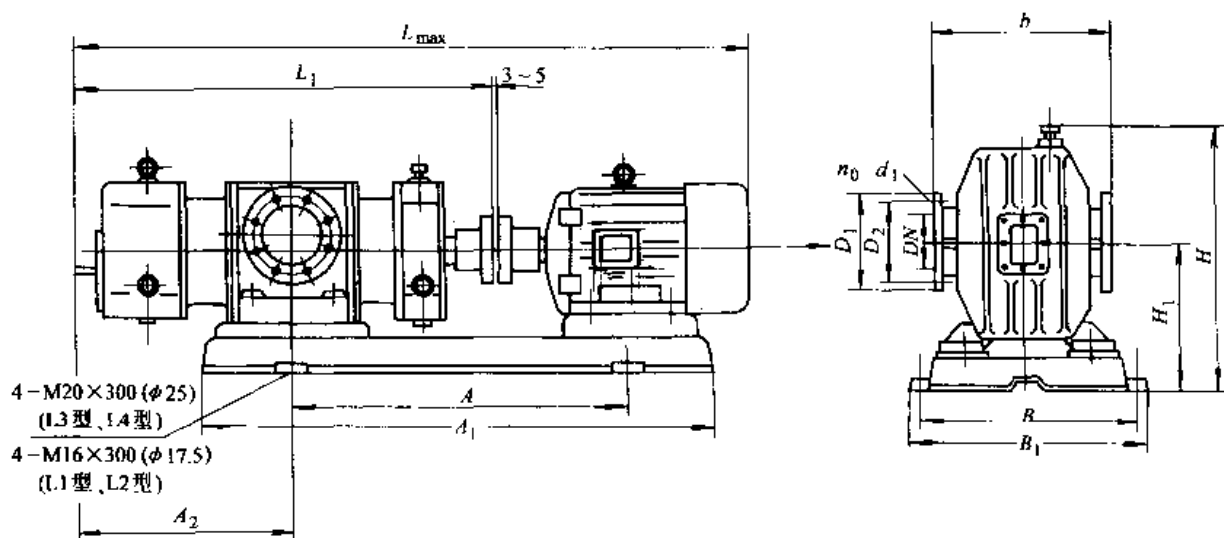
L13、…、L33LD 型罗茨鼓风机外形尺寸图
